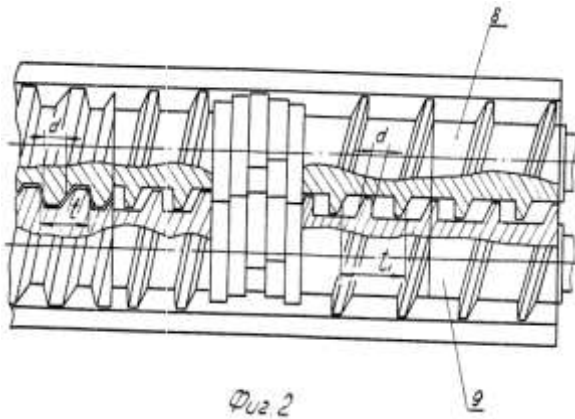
Загальний вигляд шнекового пресу із двома шнековими валами (вид зверху) [131]
